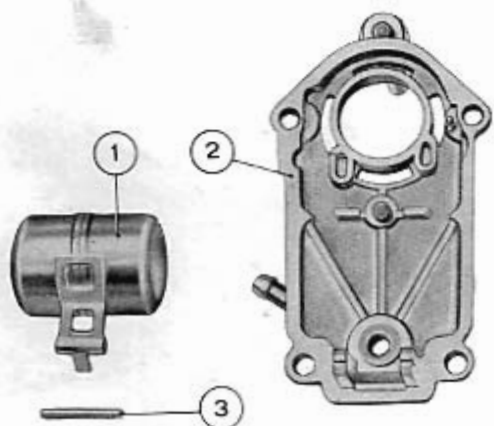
Vue éclatée du couvercle du carburateur Weber 26 IMB 1.
